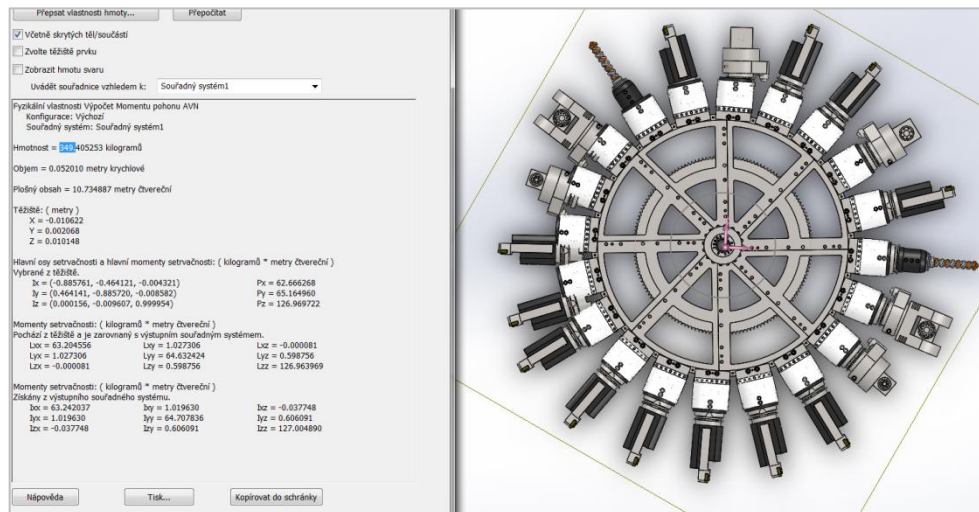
Geometrické uspořádání nástrojů na disku zásobníku
